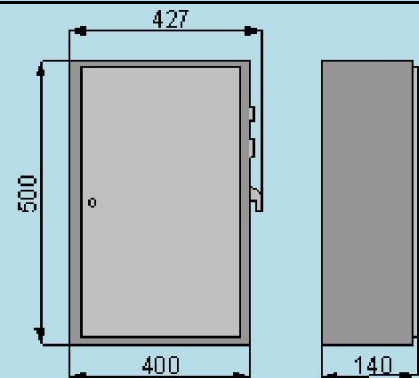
Общий вид и габаритные размеры щитков А.588Б
